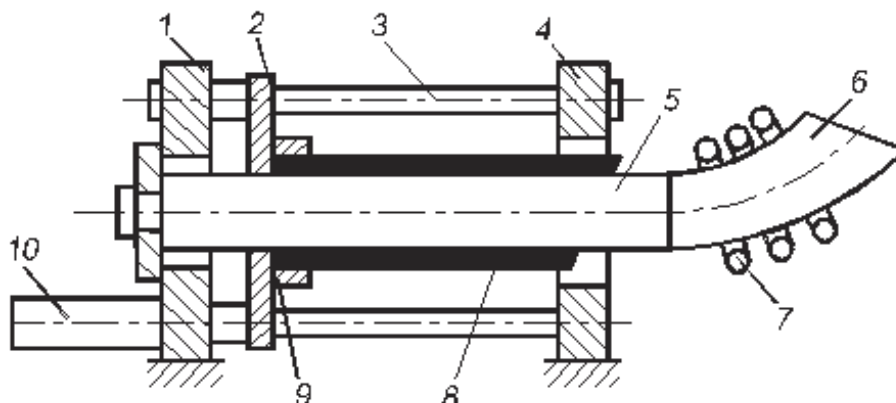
Схема устройства для изготовления крутоизогнутого патрубка
